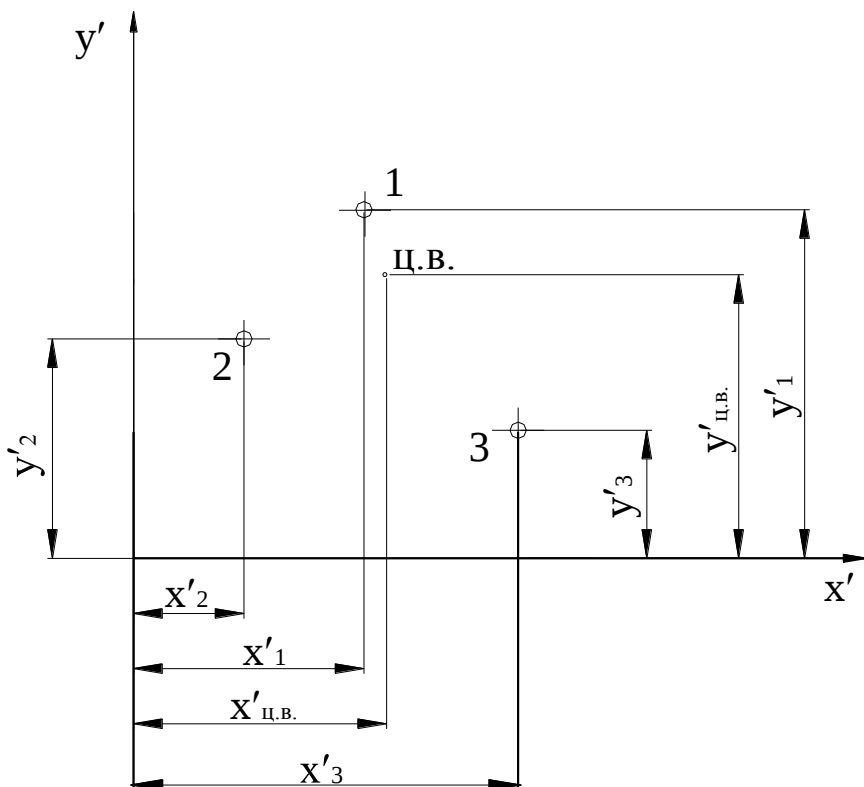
Розрахункова схема групового болтового з'єднання
